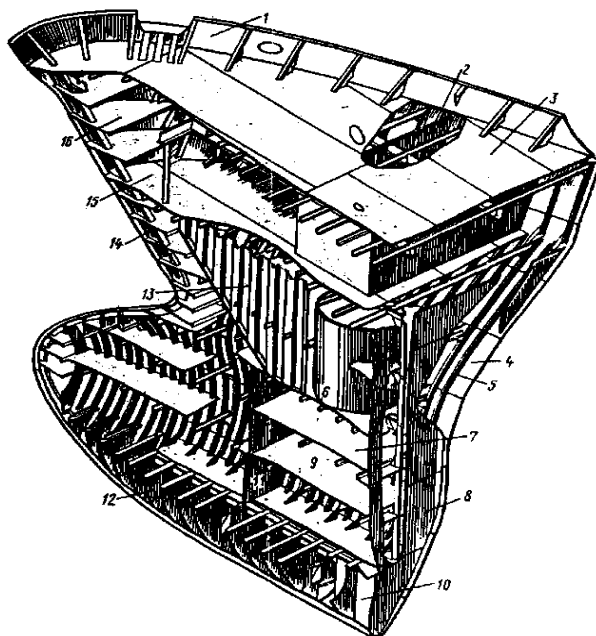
Конструкция носовой оконечности с бульбообразной наделкой: 1 - козырек; 2 - выгородка на баке; 3 - палуба бака; 4 - обшивка борта; 5 - шпангоут; 6 - цепной ящик; 7,9 - платформы; 8 - форпиковая переборка; 10 - вертикальный киль; 11 - поперечная переборка; 12 - сплошной флор; 13 - отбойная переборка; 14 - форштевень; 15 - главная (верхняя) палуба; 16 - брестук
